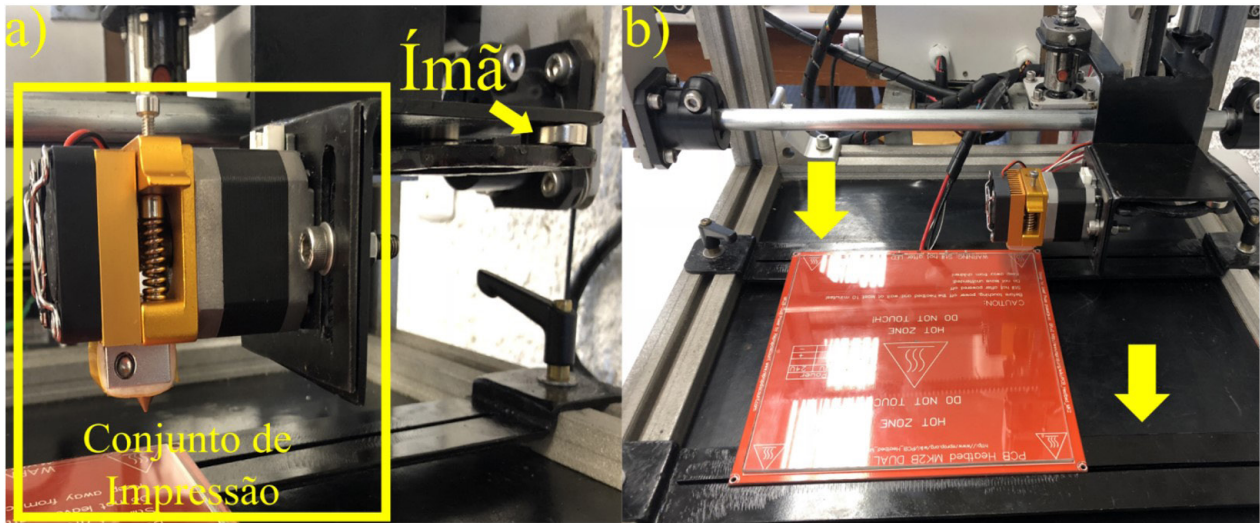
(a) Suporte de fixação do conjunto de impressão feita por ímãs. (b) Suporte da mesa aquecida.
